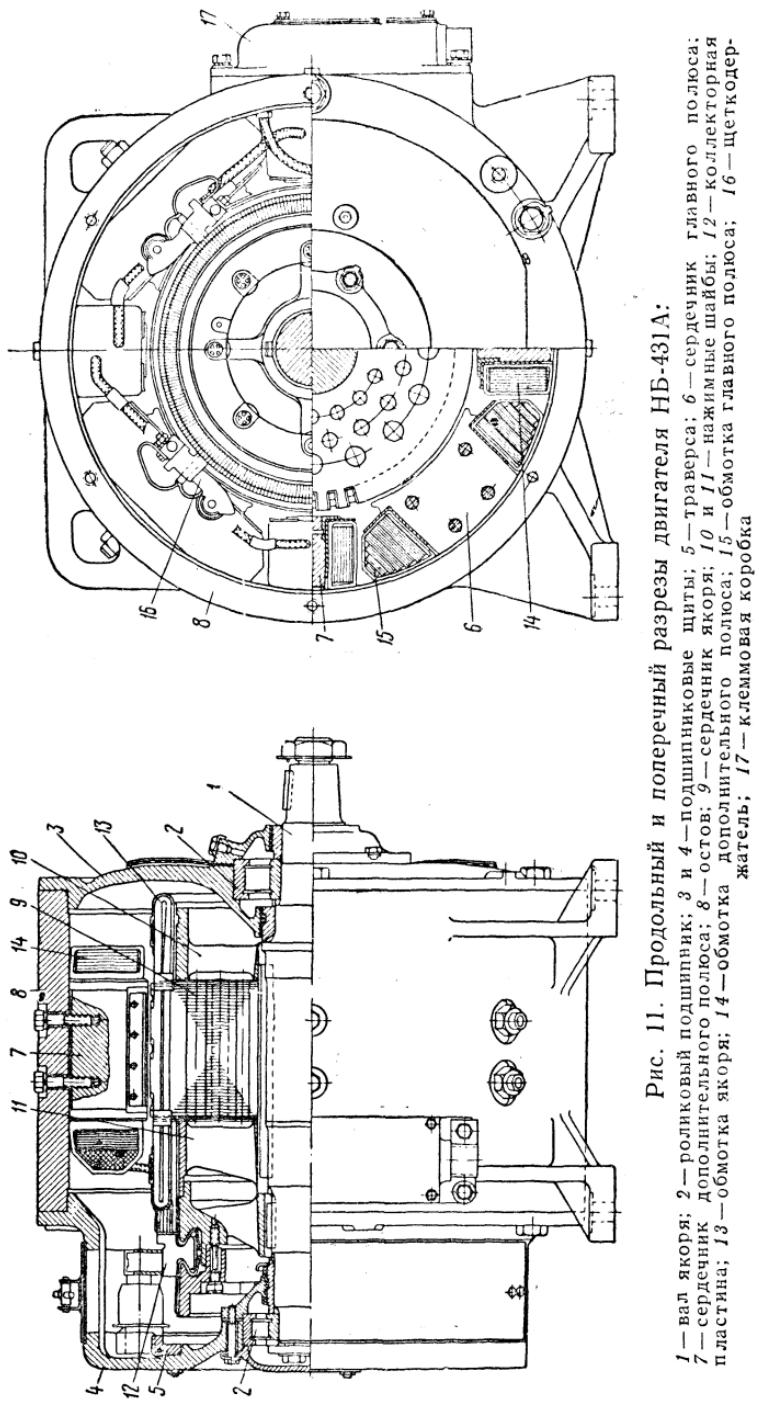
Продольный и поперечный разрезы двигателя НБ-431А:
